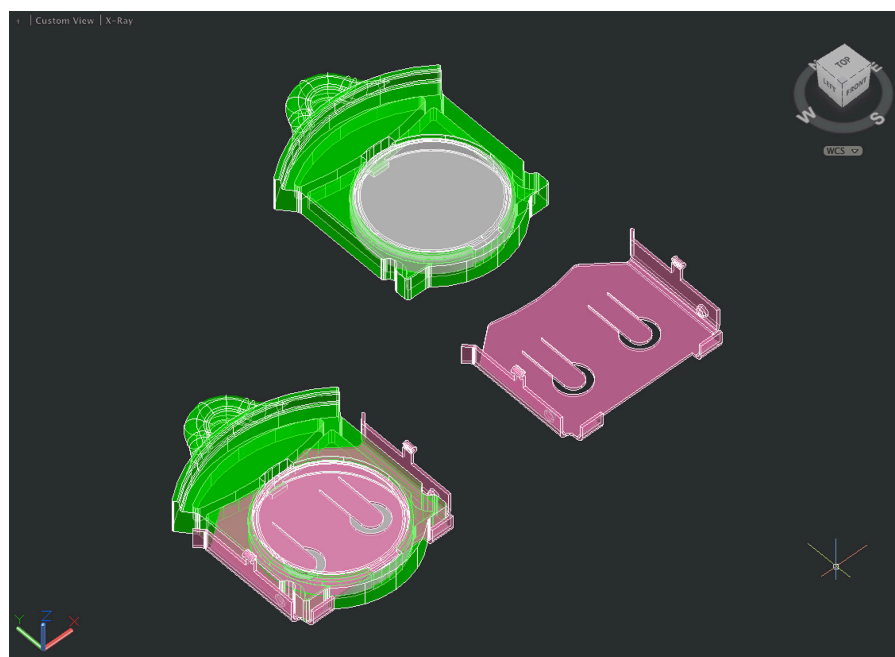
Modelos CAD 3D do suporte da bateria e da peça metálica de fixação à placa de circuitos impressos.
